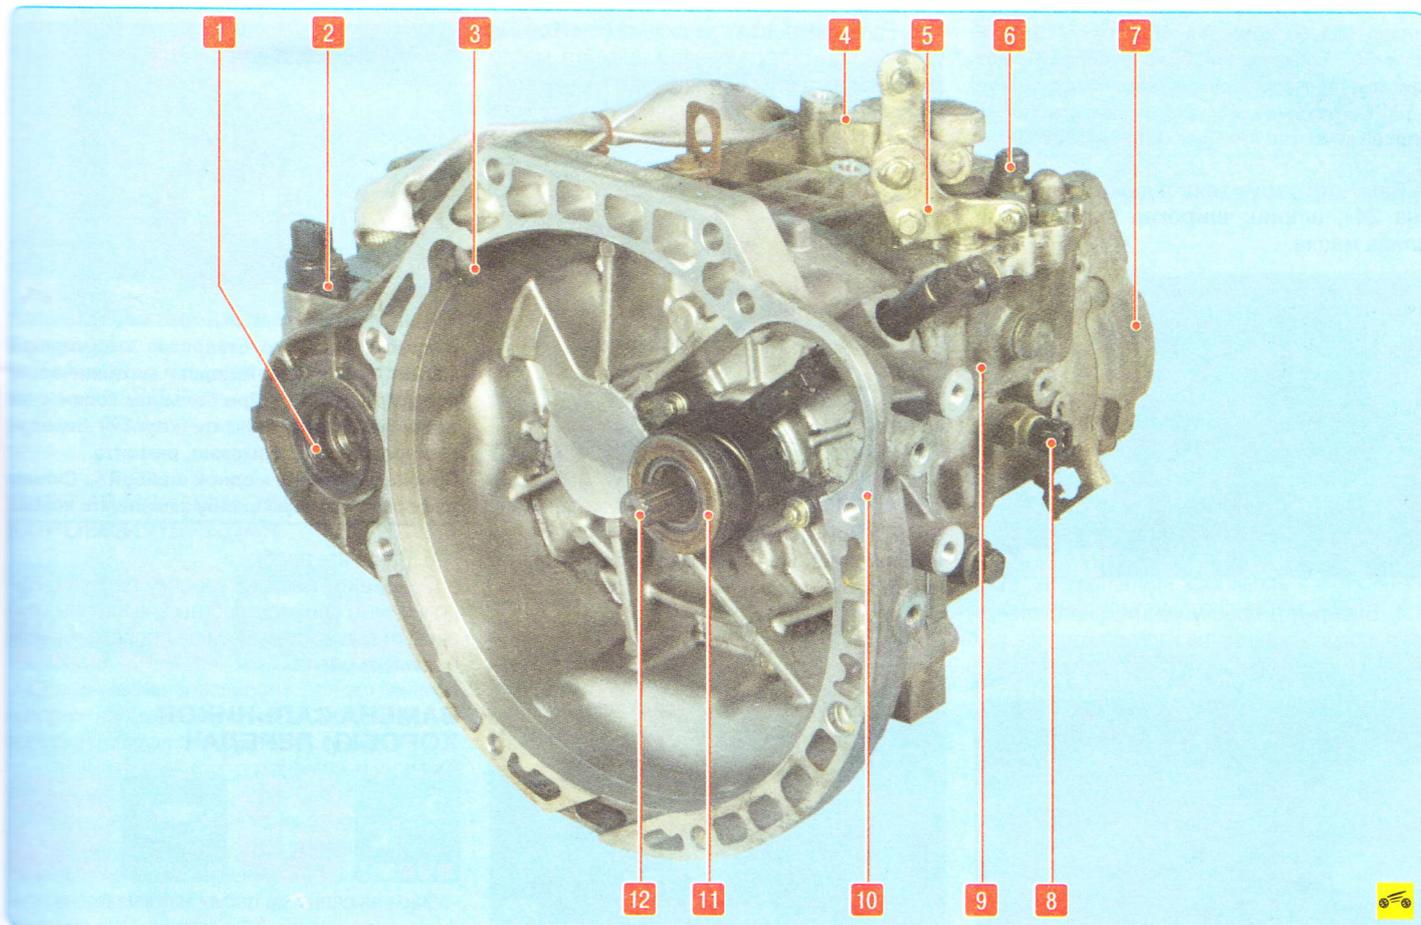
Механическая коробка передач: 1 – сальник полуоси; 2 – датчик скорости; 3 – датчик положения коленчатого вала; 4 – рычаг переключения передач; 5 – рычаг выбора передач; 6 – сапун; 7 – задняя крышка коробки передач; 8 – выключатель света заднего хода; 9 – картер коробки передач; 10 – картер сцепления; 11 – подшипник выключения сцепления; 12 – первичный вал
